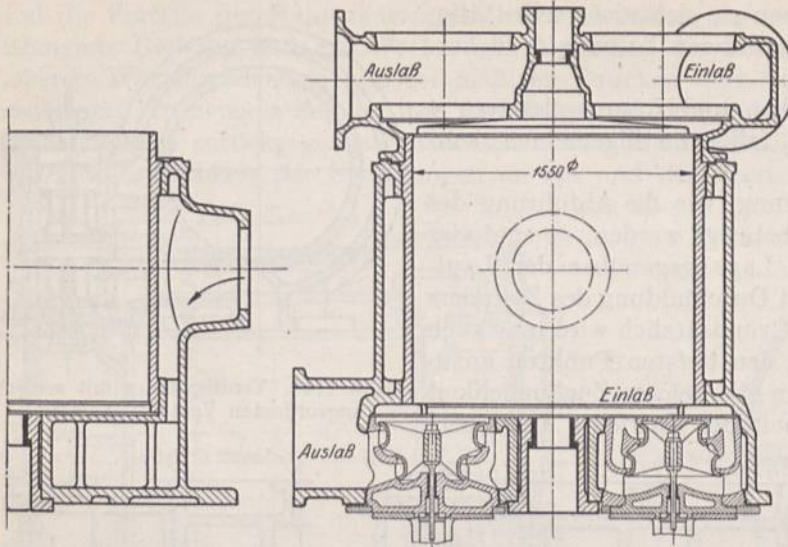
Zylinder mit Ventilsteuerung für stehende Maschinen.
